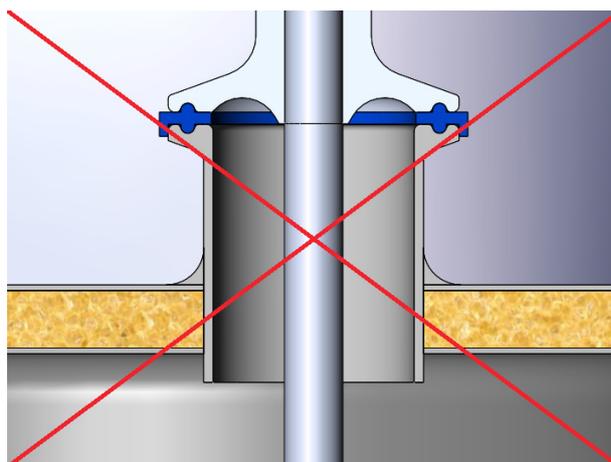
Intérieur soudé et poli de manière non affleurante
